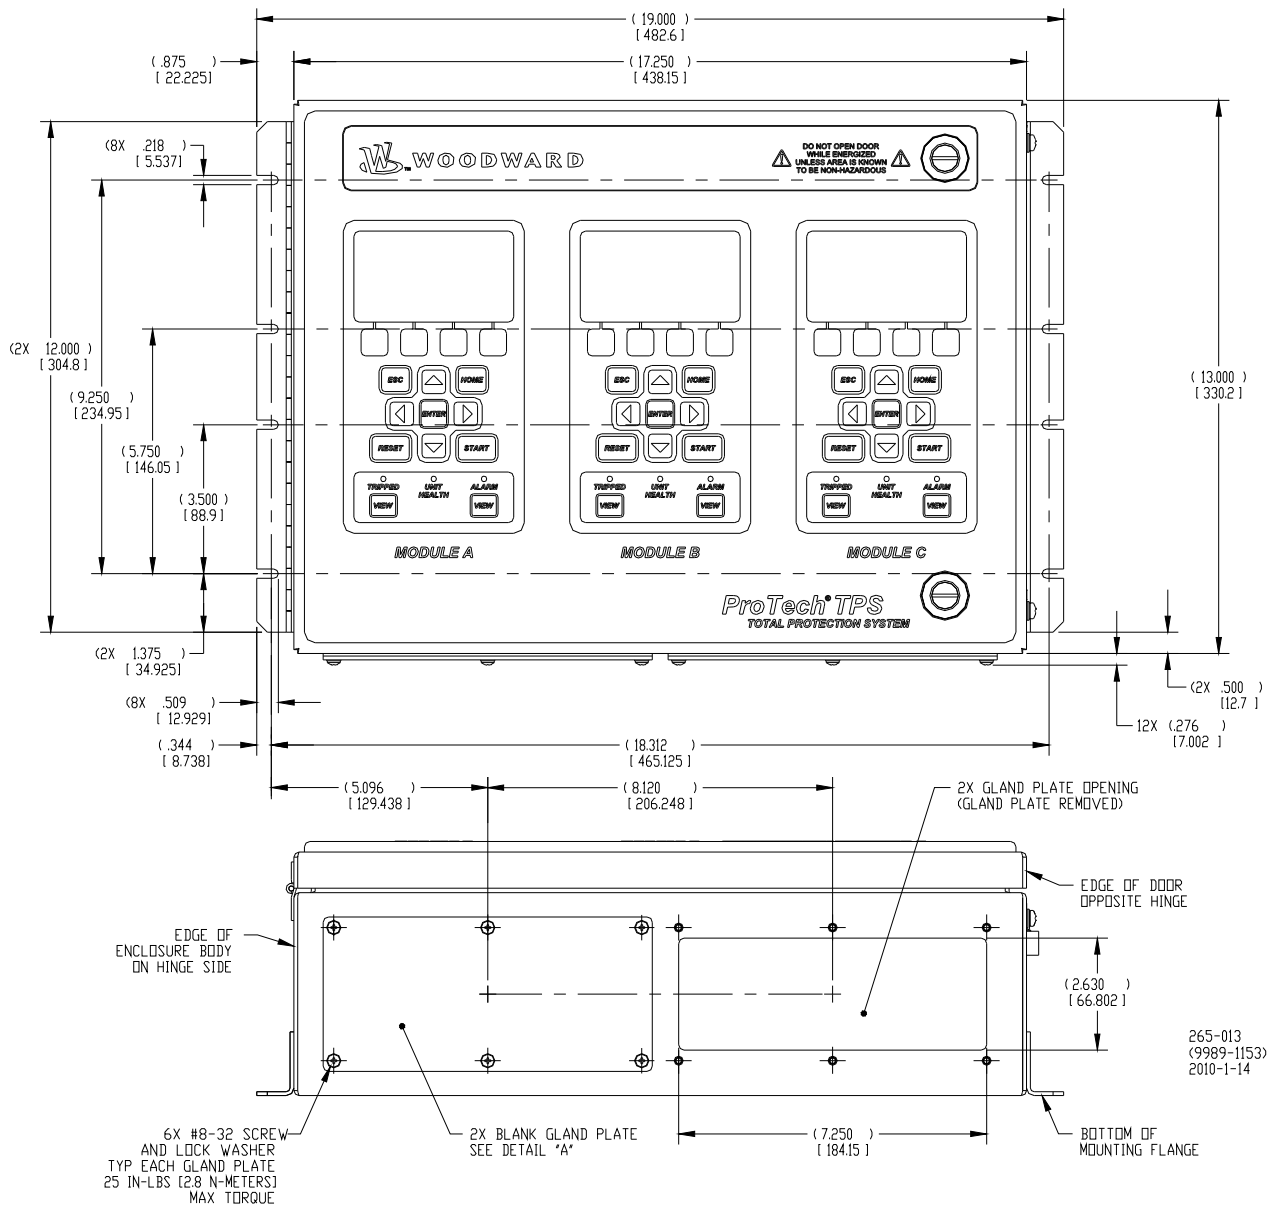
Габаритная установочная схема моделей для монтажа на стену или опору
